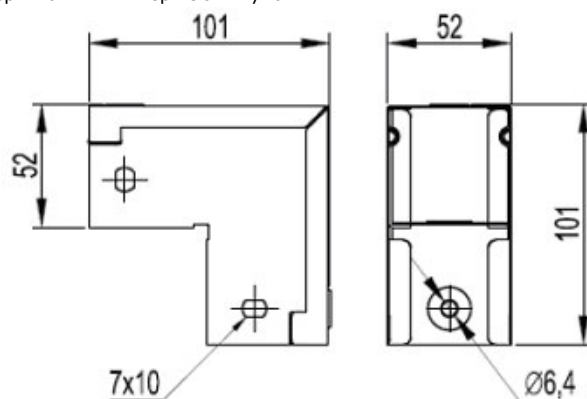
Угол вертикальный вниз 90° глухой
